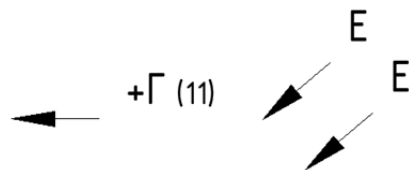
Вид и вид с дополнительной стрелкой
